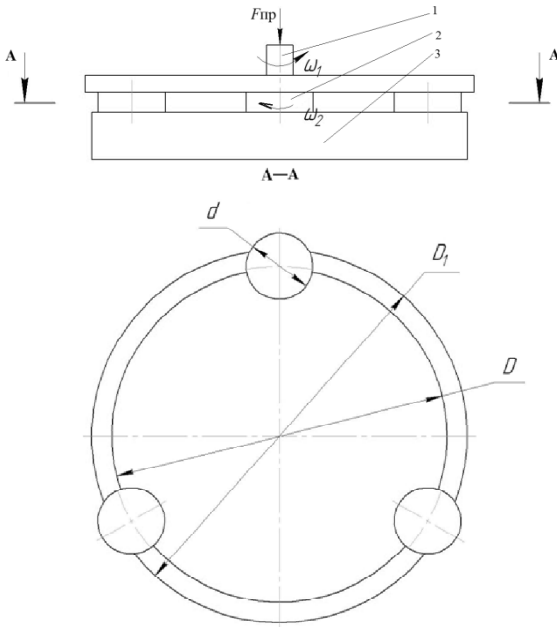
Схема притирки кольцевых поверхностей фланцев на вертикальном притирочно-доводочном станке:
